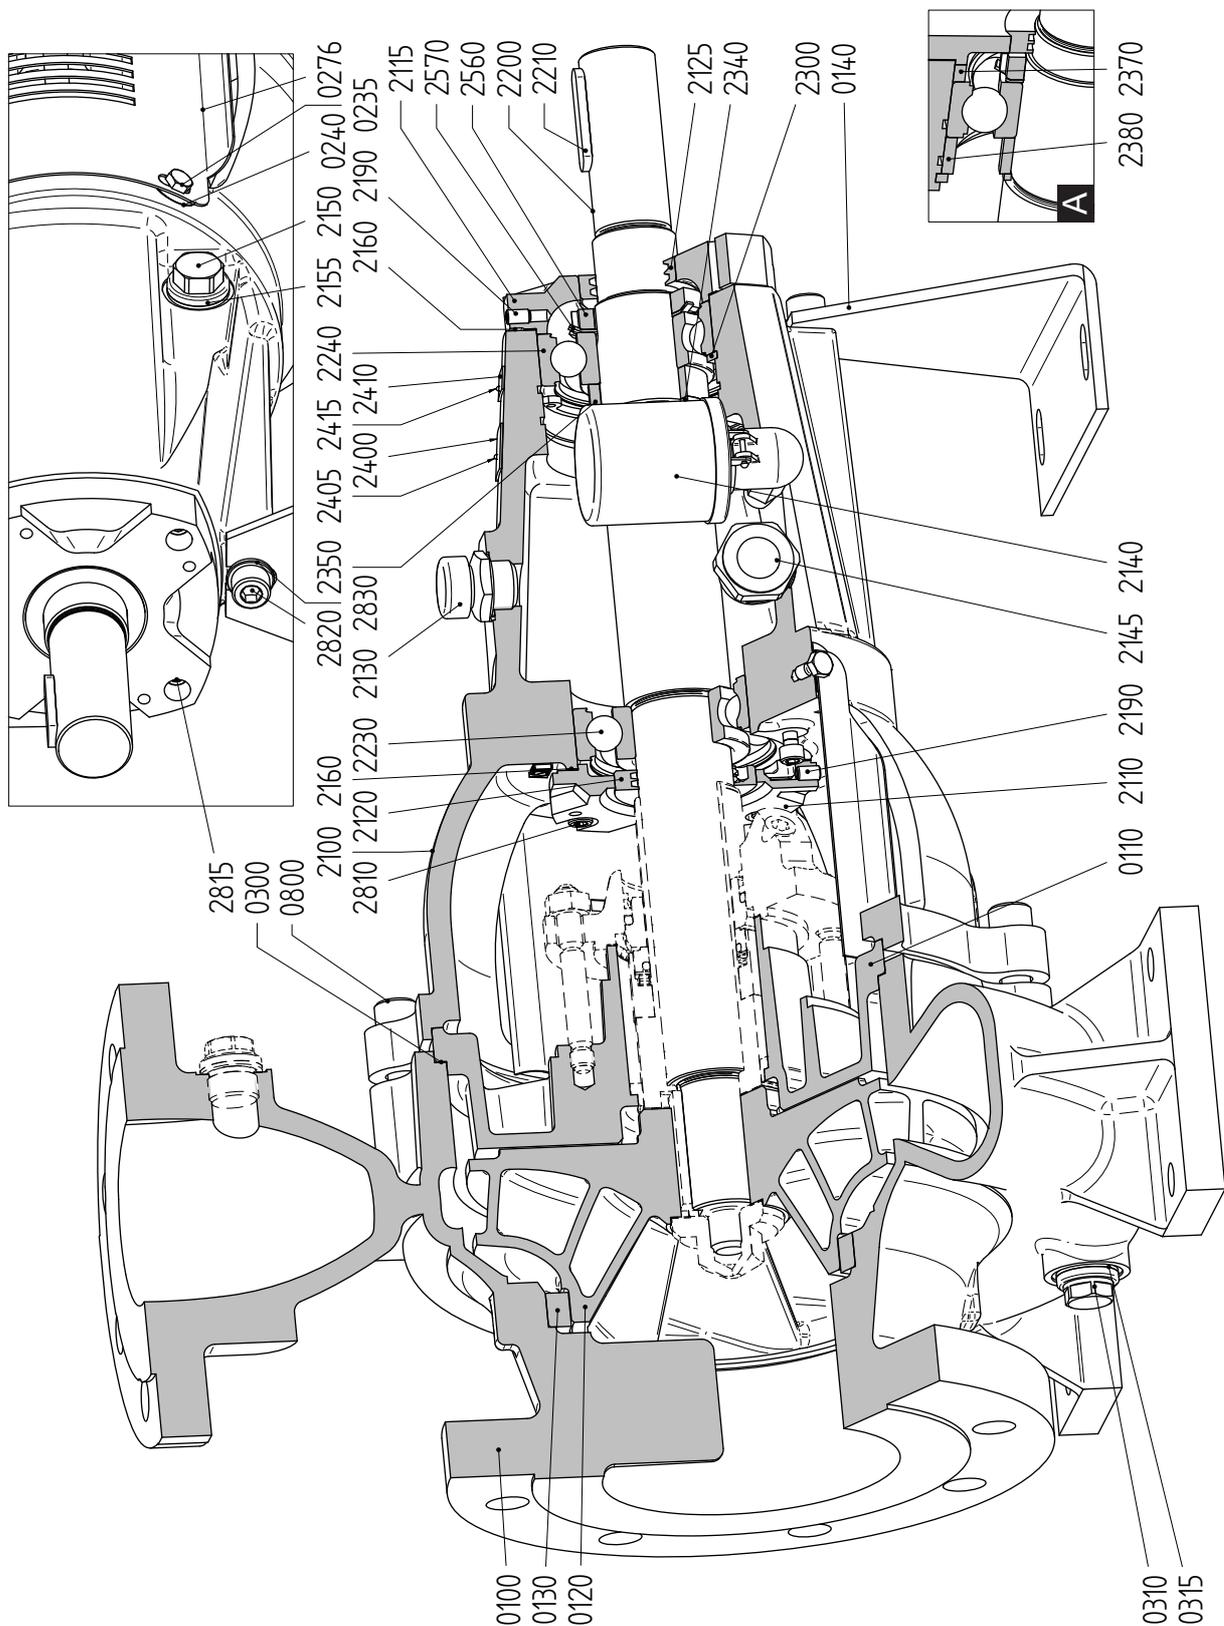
Schnittzeichnung L3 (A = für Lagergruppe 3).
